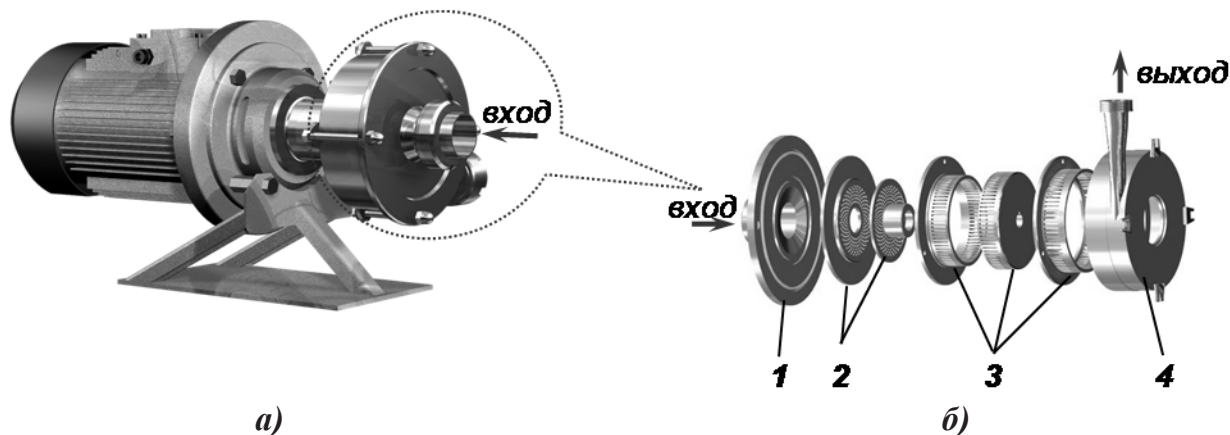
Общий вид дисково-цилиндрического аппарата типа АР-3000 (а) и его узлов (б): 1 – крышка; 2 – статорно-роторный дисковый узел; 3 – статорно-роторный цилиндрический узел; 4 – корпус с выходным патрубком.
